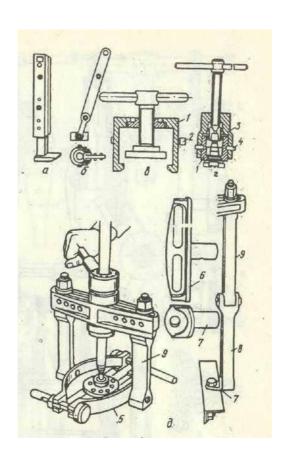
Простые составные захваты: а – раздвижной лапчатый; 6 – захват с шайбой; в и г – составные неподвижные; д – со сменными захватами; 1 – захват; 2 – кольцо; 3 – корпус; 4 – вилка; 5 – 7 – сменные захваты; 8 – удлинитель; 9 – стойка
